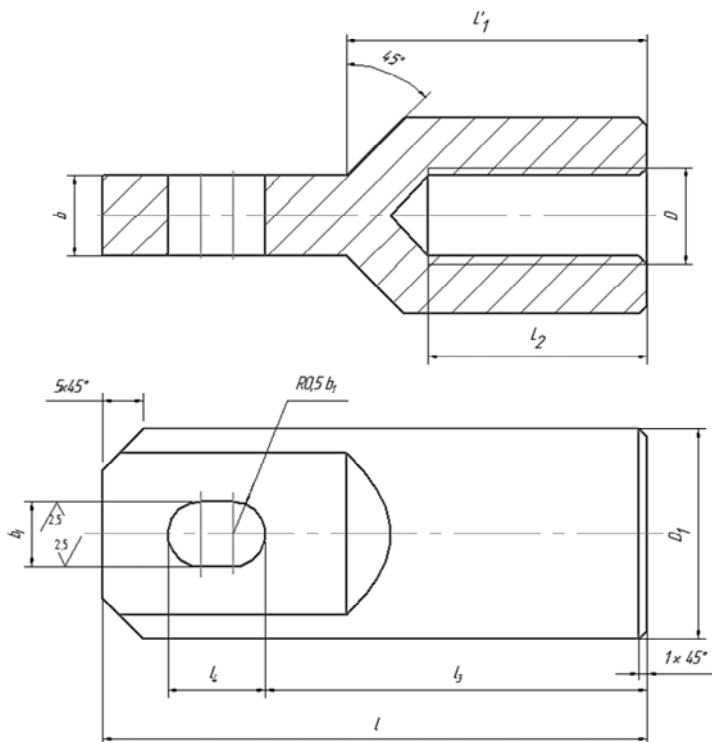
Конструкция тяги гидравлического приспособления для удаления стержней
